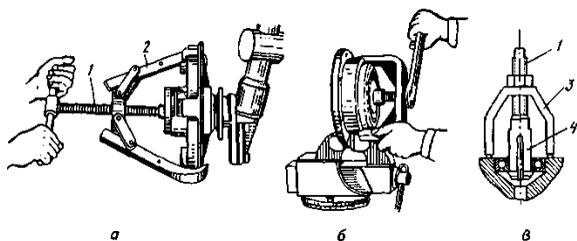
Приемы снятия ступицы колеса универсальным съемником (а), выпрессовки кольца роликового подшипника специальным съемником (б) и схема специального съемника для выпрессовки шарикового подшипника из глухого гнезда (в); 1 – винт; 2 – лапчатый захват; 3 – упор; 4 – цапга
